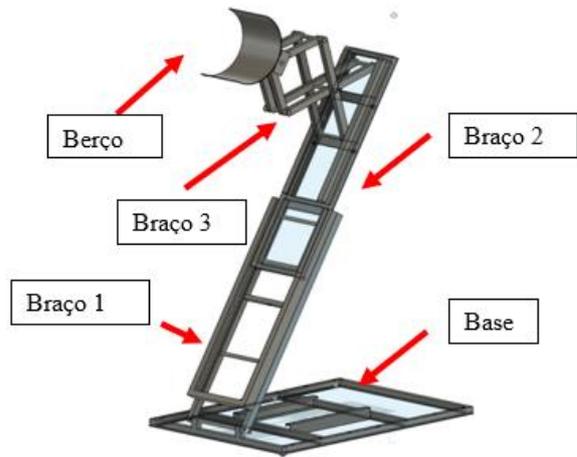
Desenho e montagem das partes que constituem o braço mecânico.
